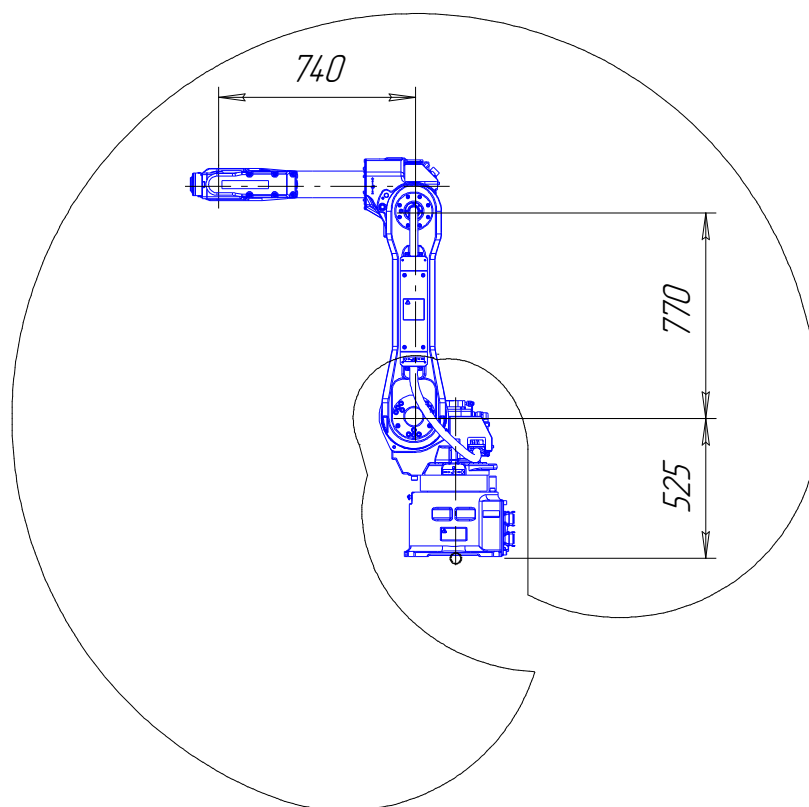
Манипулятор робота для дуговой сварки AM 120iB (FANUC)
